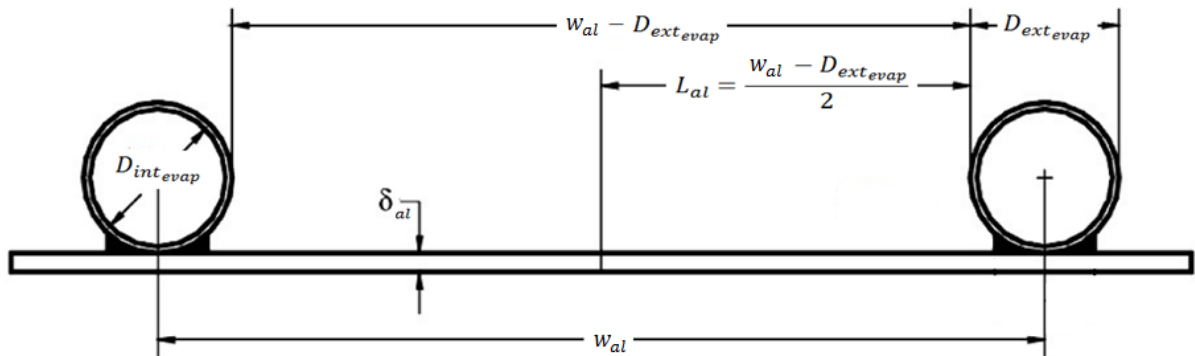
Dimensões da placa e tubo comportando como aleta
